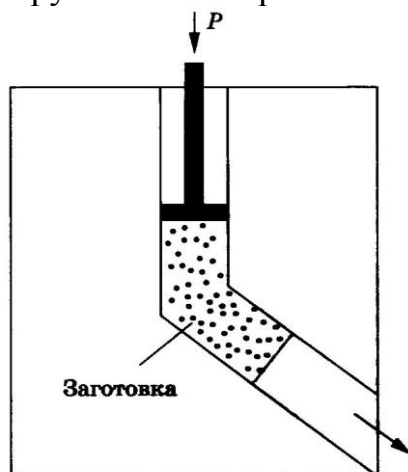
Принцип способа равноканального углового прессования. [5]
